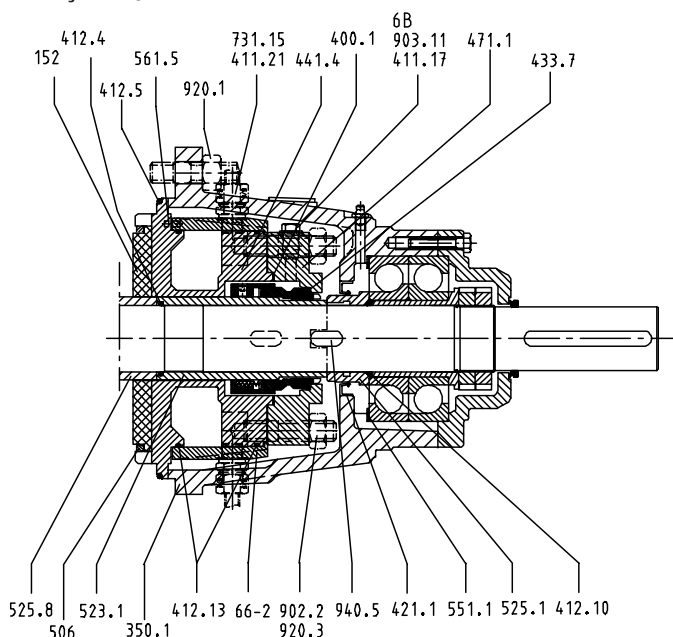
Desmontar o empanque mecânico refrigerado com água
